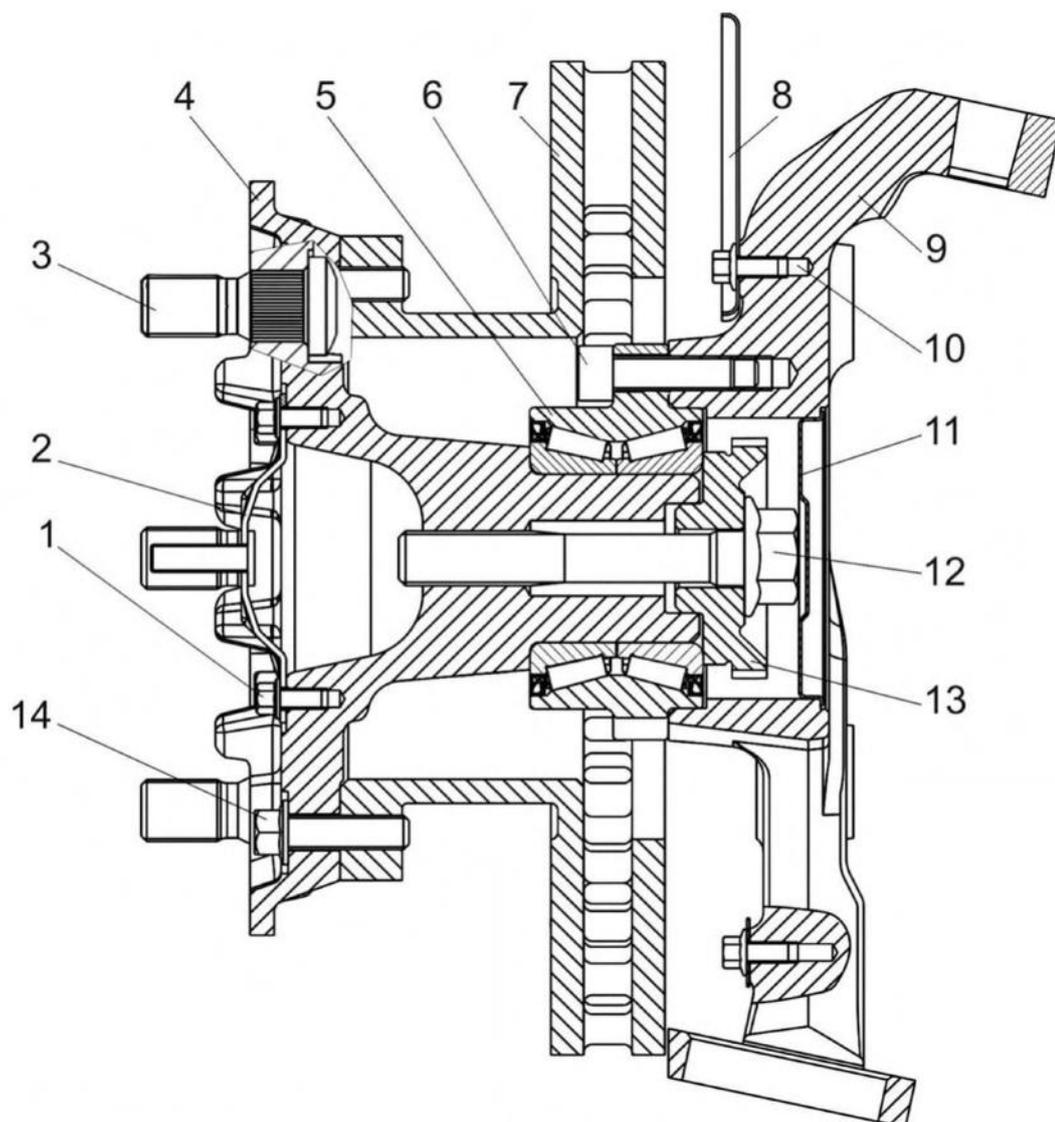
Стойка со ступицей: 1,10,12,14 – болты; 2 – кронштейн колпака колеса; 3 – болт ступицы; 4 - ступица; 5 – двухрядный роликовый конический подшипник; 6 – винты; 7 - диск тормозной; 8 – щит переднего тормоза; 9 – стойка; 11 - заглушка; 13 – ротор АБС
